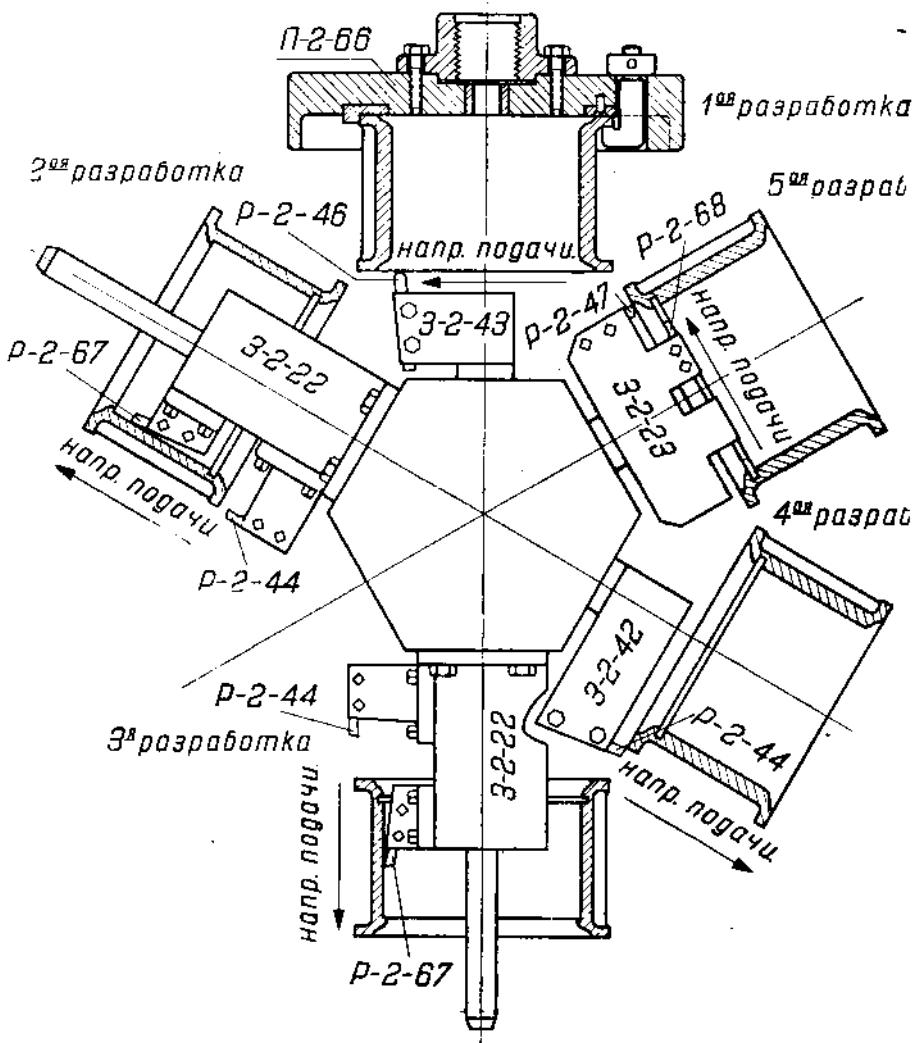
Обработка корпуса электромотора на револьверном станке.
